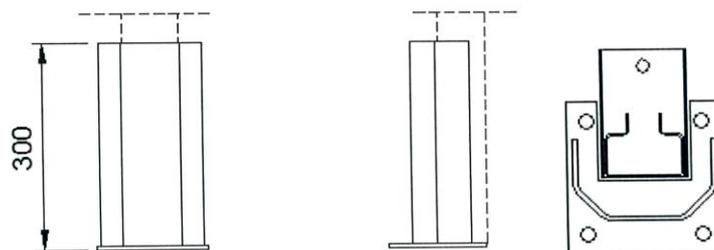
Protetor de coluna (vistas frontais e planta (ABNT NBR 15524-1).
